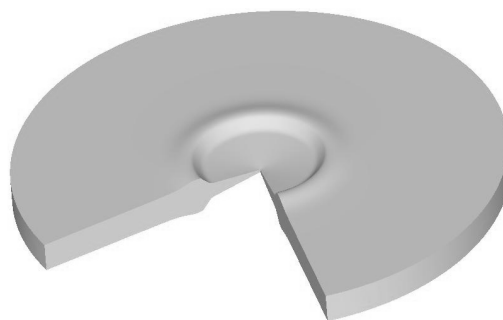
Здеформована заготовка в розрізі після видавлювання
